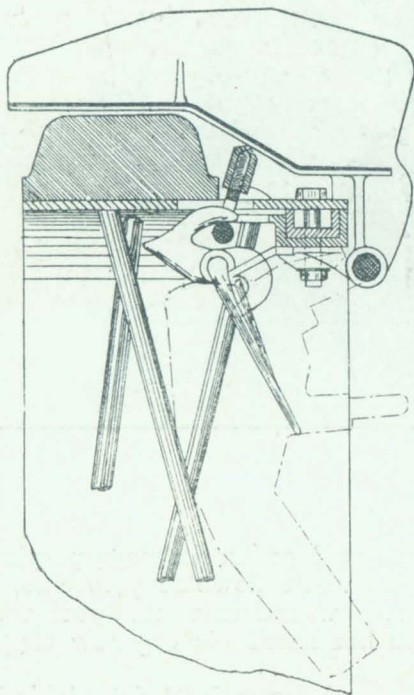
Schemat ruchomego połączenia dwu części podwozia Pavesi.
